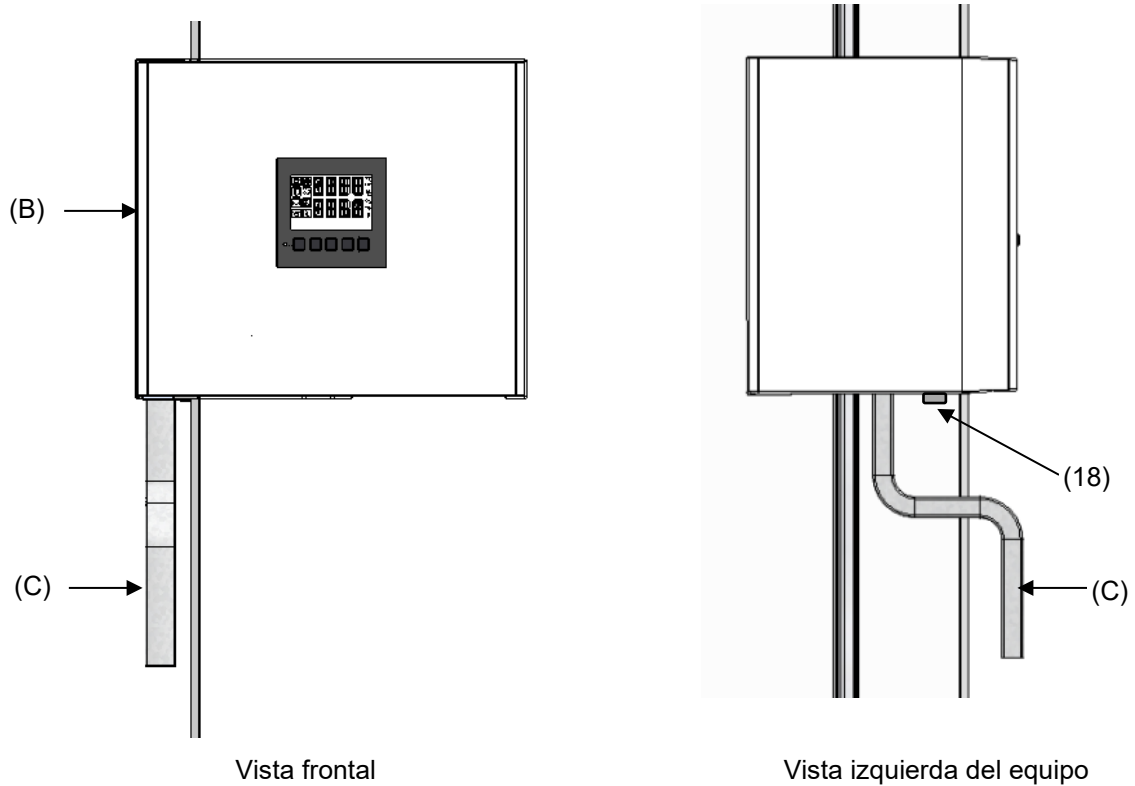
Carcasa de cierre y regulador con panel de control del regulador y manija de la puerta
